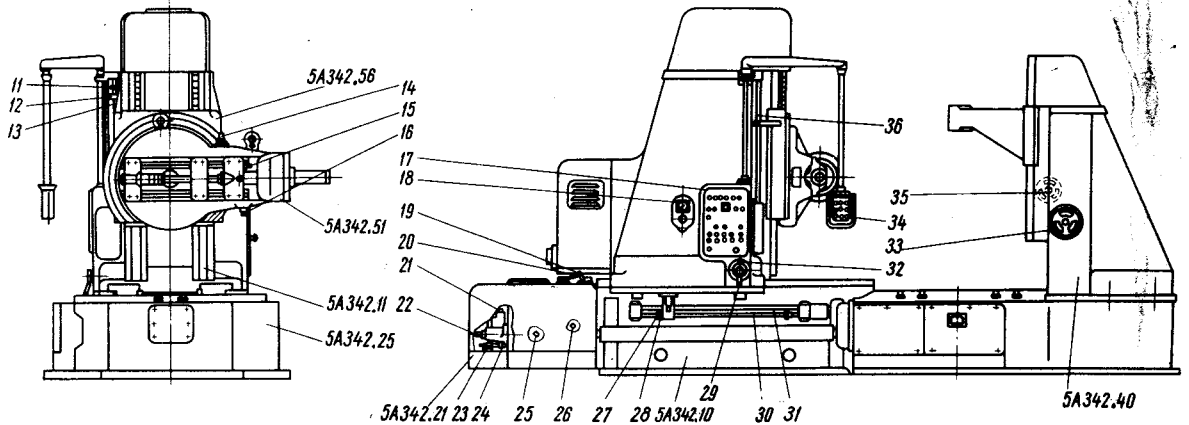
Рис. II. Общий вид станка с обозначением органов управления и основных узлов:
